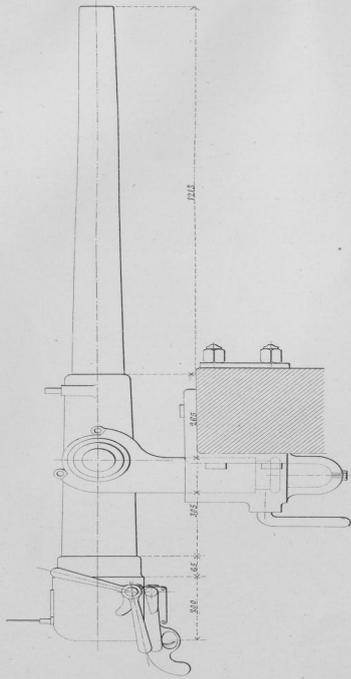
Coupe longitudinale du tube. Echelle 1/2
